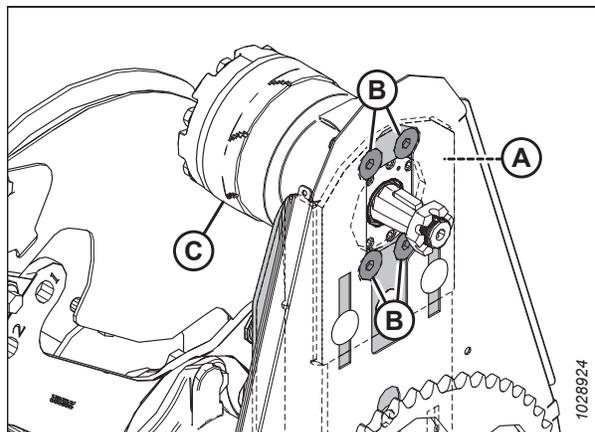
Viti di montaggio del motore di trasmissione dell'aspo
